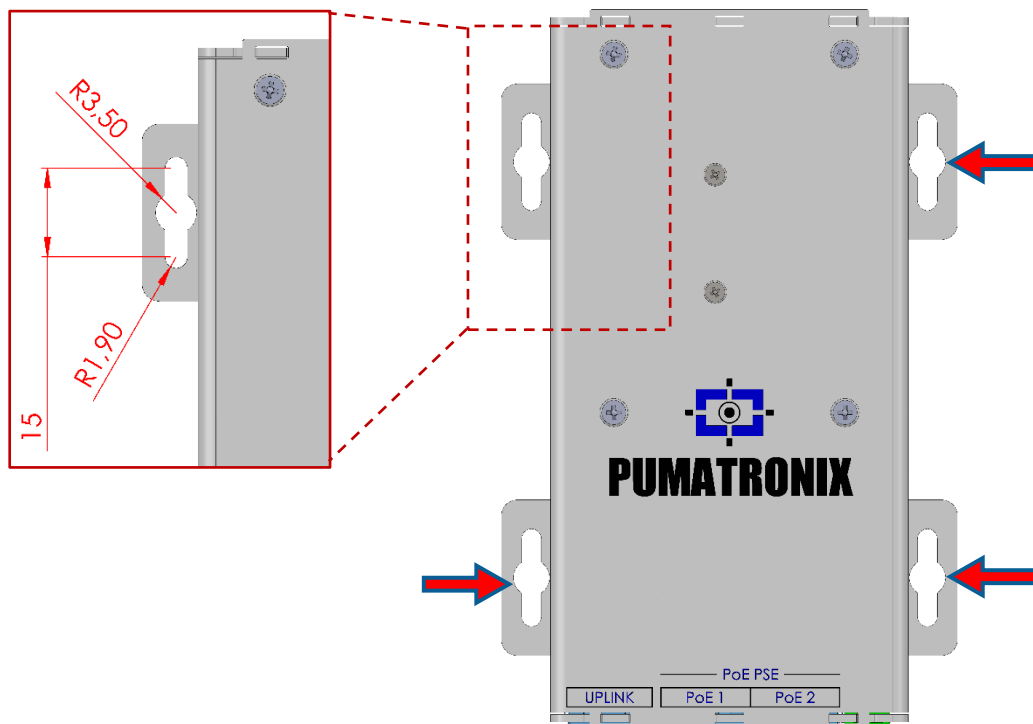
VISTA SUPERIOR COM A POSIÇÃO DAS ABAS PARA FIXAÇÃO
